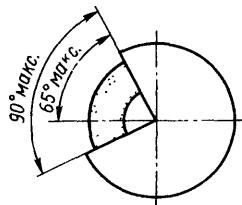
Расположение и наибольший угол раскрытия защитного кожуха заточного станка
